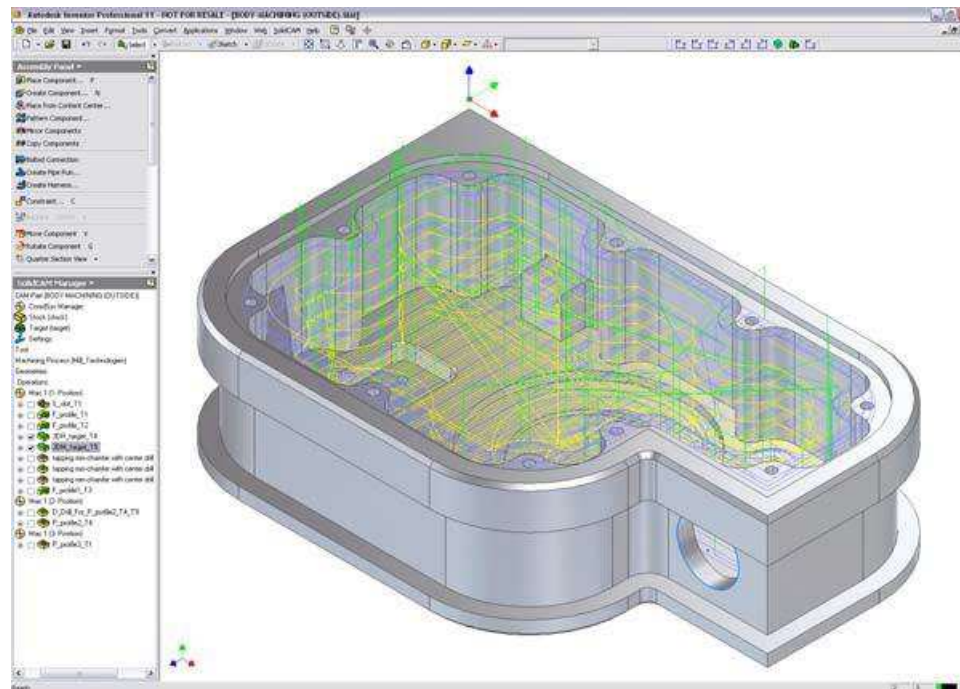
Фрезерна обробка в режимі 2D
